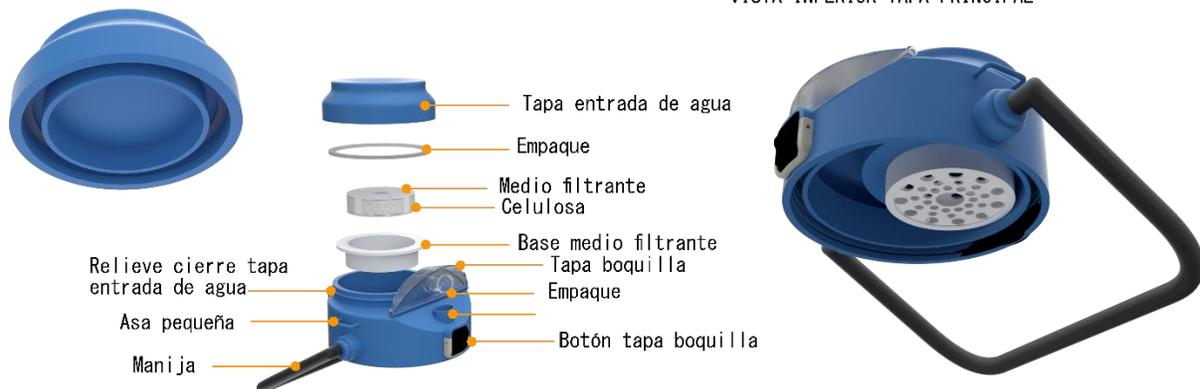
Despiece tapa principal producto final. Fuente: Autora
